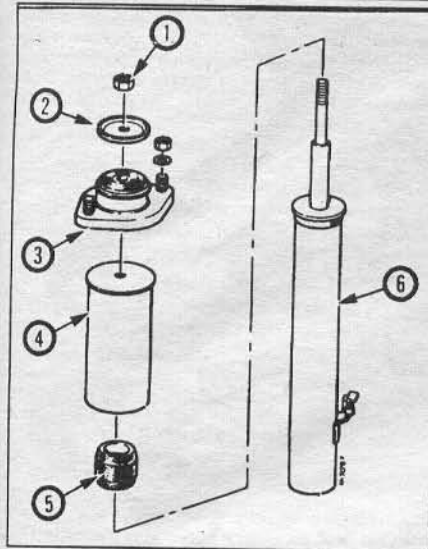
а Сборка стойки (модели выпуска 1984 - 1987 годов): 1 - гайка крепления амортизатора; 2 - шайба; 3 - проставка; 4 - кожух; 5 - резиновый ограничитель хода; 6 - стойка.
